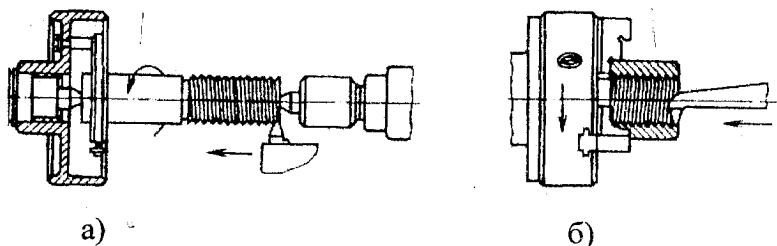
Схема нарізання різі різцем на токарному верстаті:
